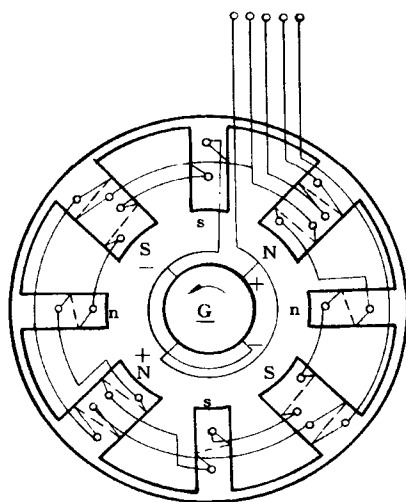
AX3-300-2 型直流焊接发电机电气线路图
